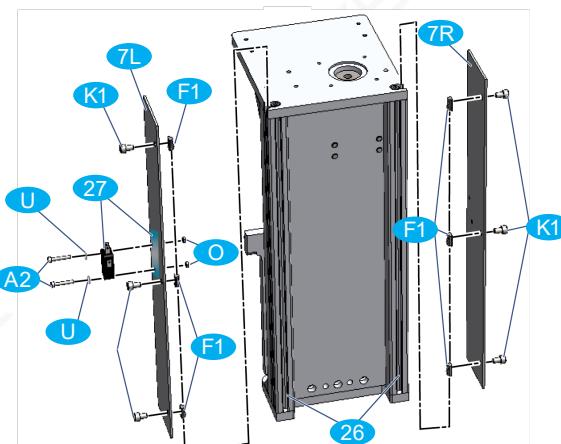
Montage Aussteifungen und Z-Referenzschalter
